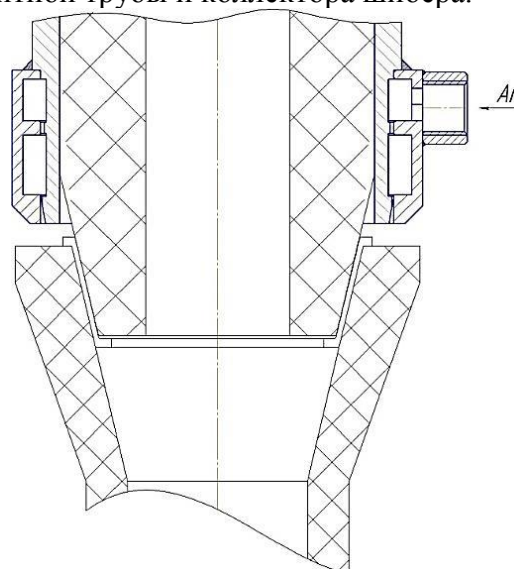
Конструкция выходного патрубка коллектора шибера стальковша
